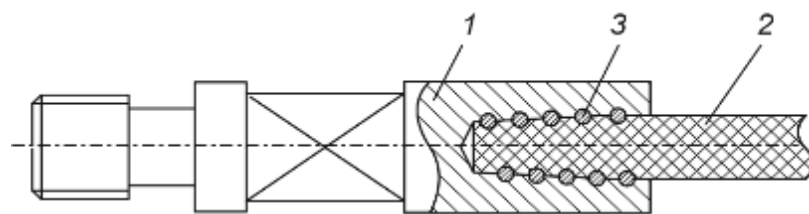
З'єднання сталевго головки насосної штанги з полімерно-комполитним стрижнем: 1 – сталева головка; 2 – кінець стрижня насосної штанги; 3 – вставний сталевий виток
